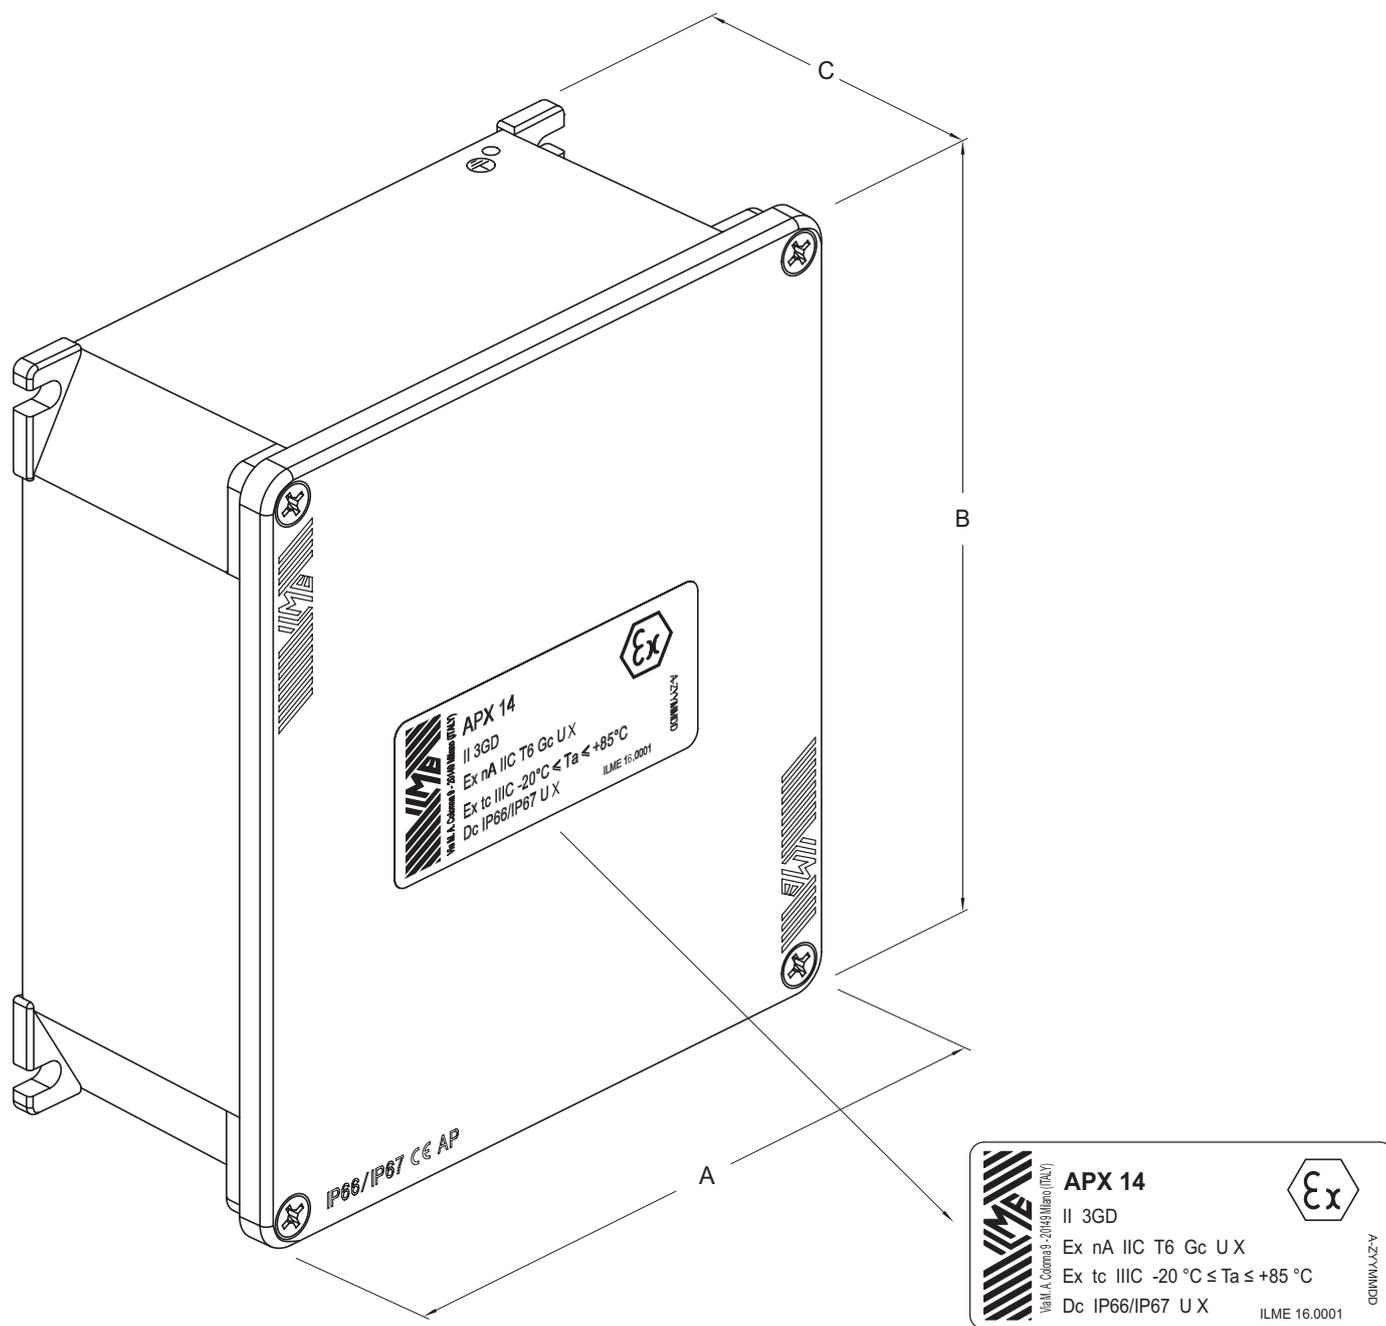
Vista prospettica con dettaglio esempio targa dati
